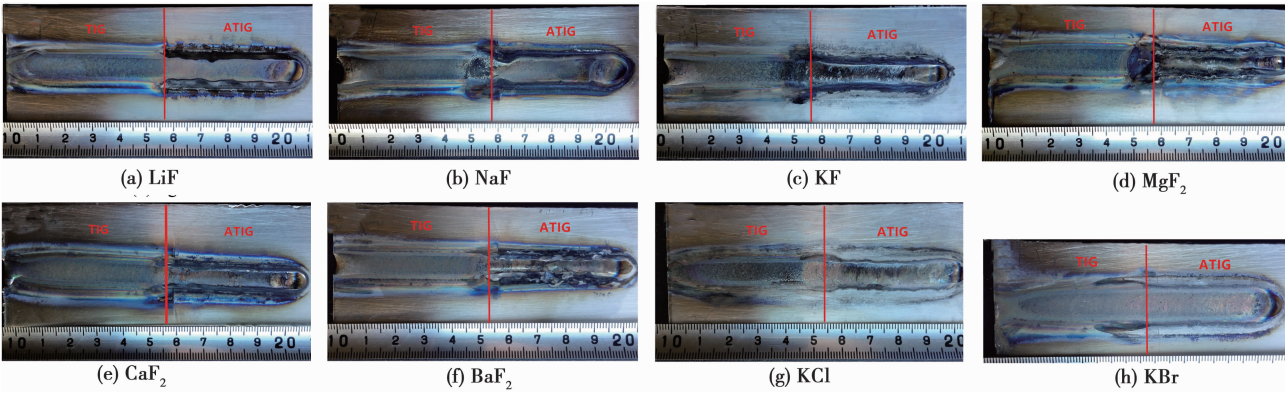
TIG 焊和 ATIG 焊焊缝外观成形
